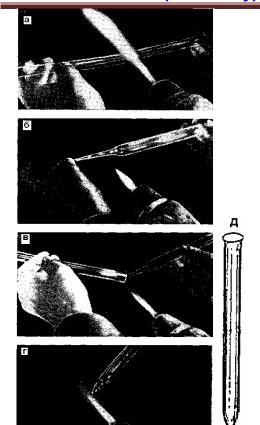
Изготовление заготовки бюретки без крана: а—приготовление заготовки; б— формирование оливки на одном конце; в— оплавление и развертывание второго конца; г—оплавление и отжиг конца бюретки; д —готовое изделие.
